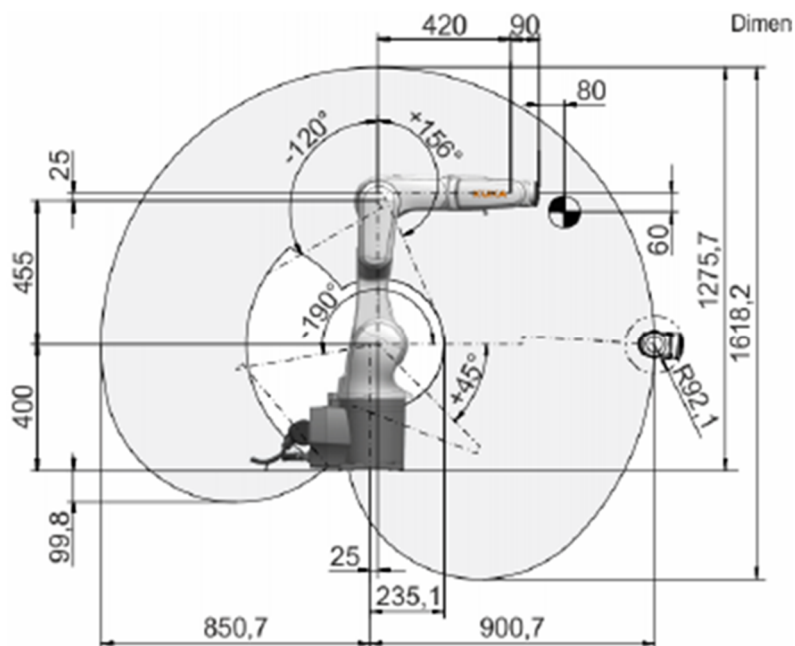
Рабочая зона робота-манипулятора KUKA KR6 R900 sixx
